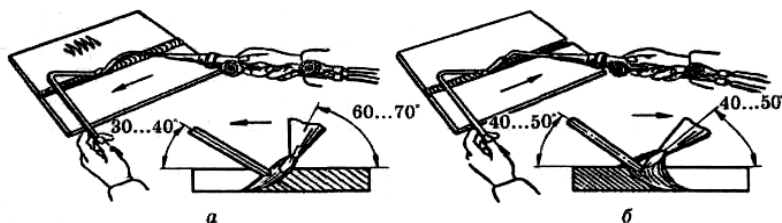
Способи газового зварювання залежно від положення полум'я пальника:
